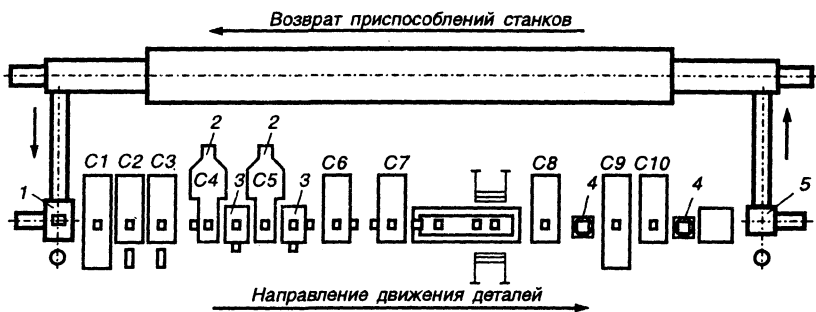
Схема ПАЛ для обработки корпусов редукторов
